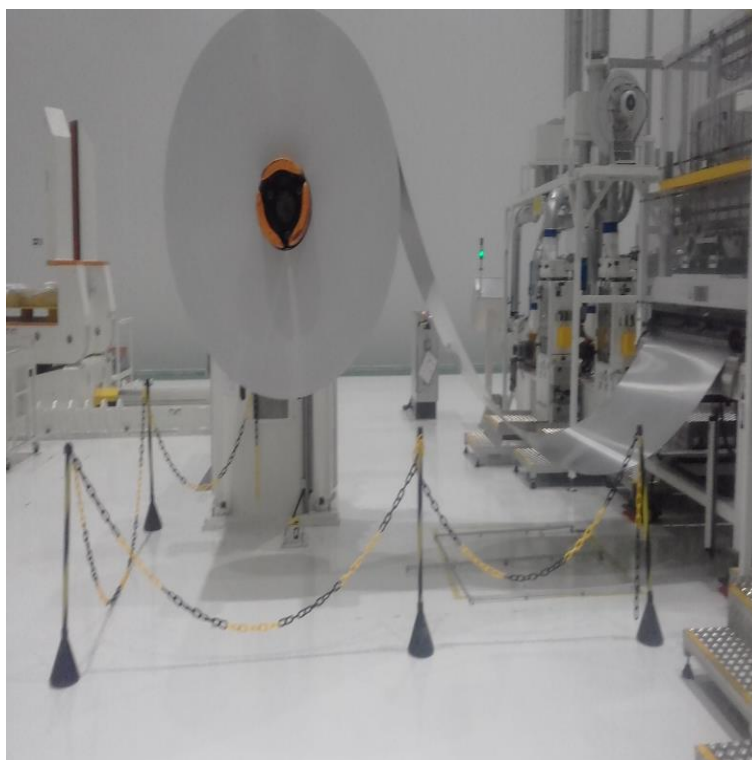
Painel de Controle Sistema de Tombador da Bobina, Carro de Transporte e Desbobinador
